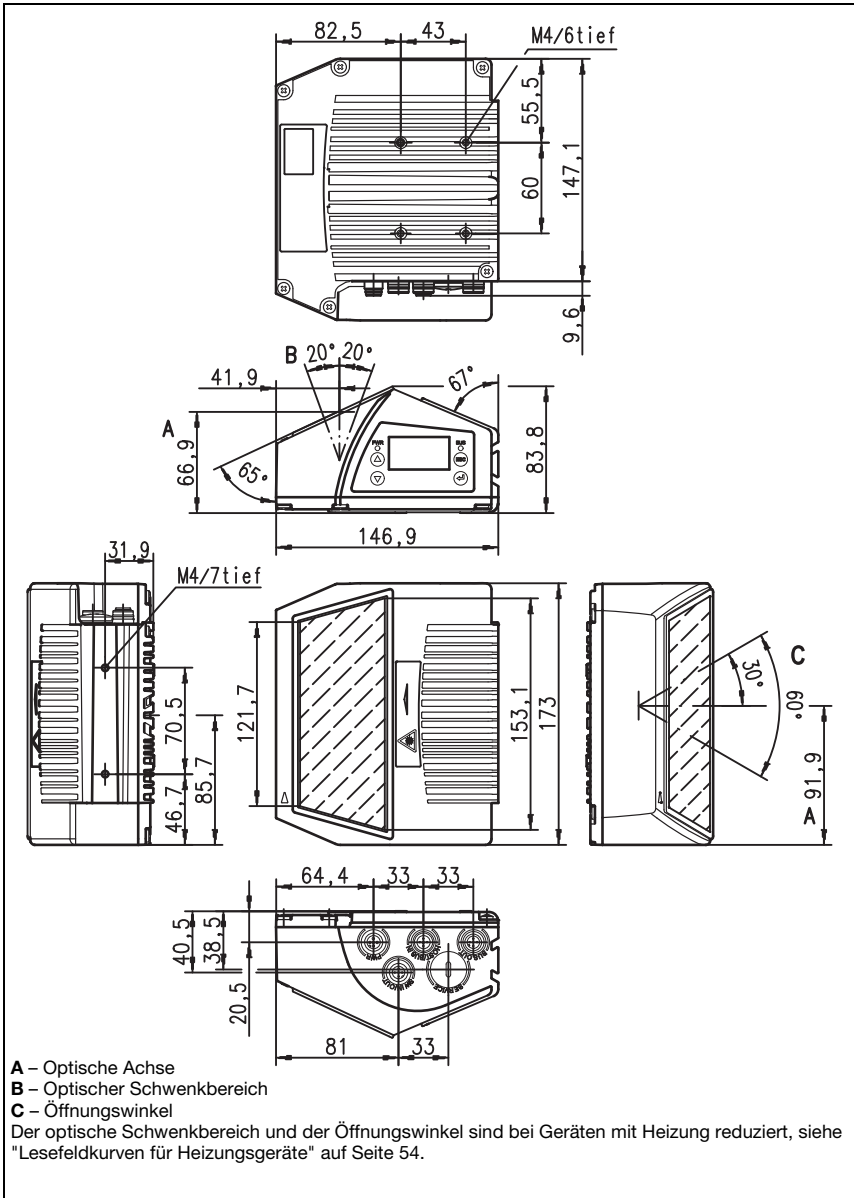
Maßzeichnung Scanner mit Schwenkspiegel BCL 558*i* 0...100
